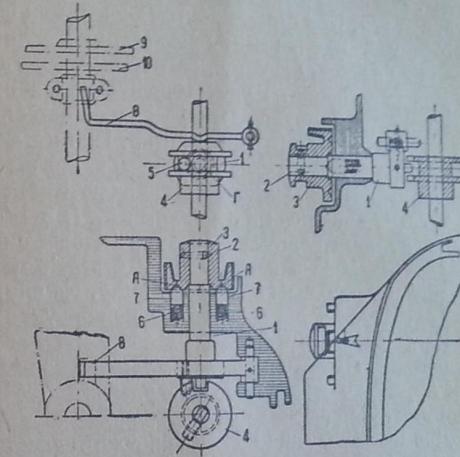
Подъемный механизм реверсивно-тормозного барабана контроллера ДТ-41.
